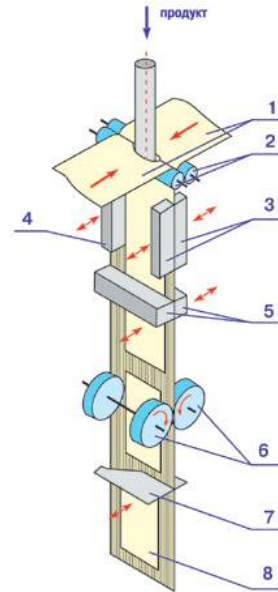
Компонування машини з губками зварювання і роликми протяжки: 1 – плівка; 2 – направляючі валки; 3, 4 – губки поздовжнього зварювання; 5 – губки поперечного зварювання; 6 – ролики протяжки; 7 – відрізний ніж; 8 – готовий пакет
